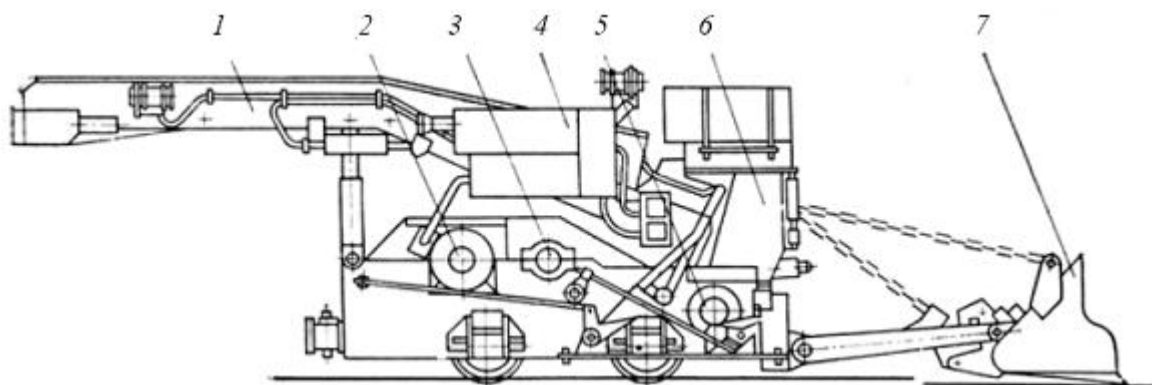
Погрузочная машина ППН-5Э: 1 – перегрузочный ленточный конвейер с индивидуальным электроприводом; 2 – главный электродвигатель с редуктором; 3 – механизм передвижения машины; 4 – электрооборудование; 5 – механизм подъема ковша; 6 – рама на колесном ходу; 7 – ковш
